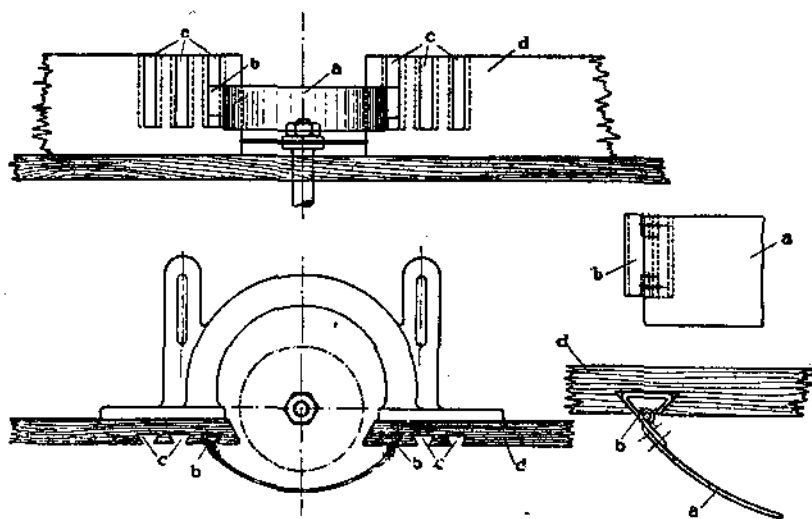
Внешний вид металлической коробки, ограждающей фрезу.
